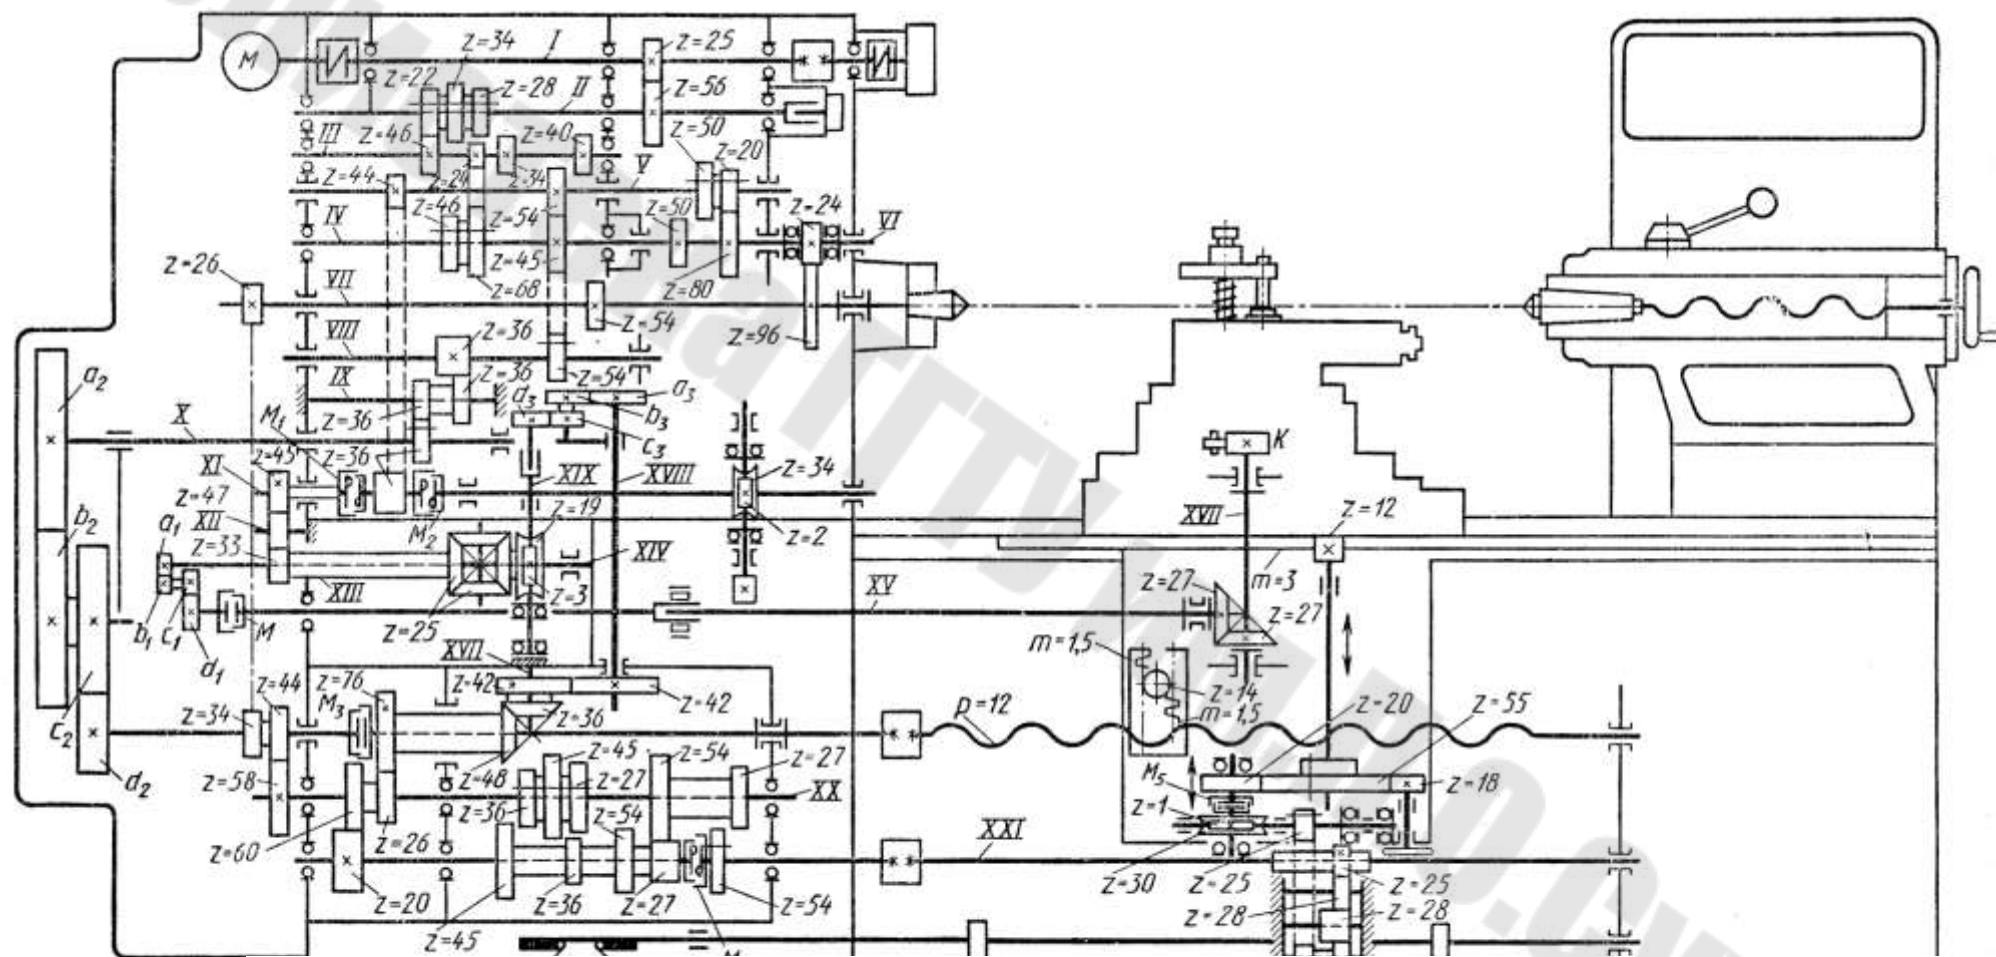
Кинематическая схема универсального токарно-затыловочного станка 1Б811
